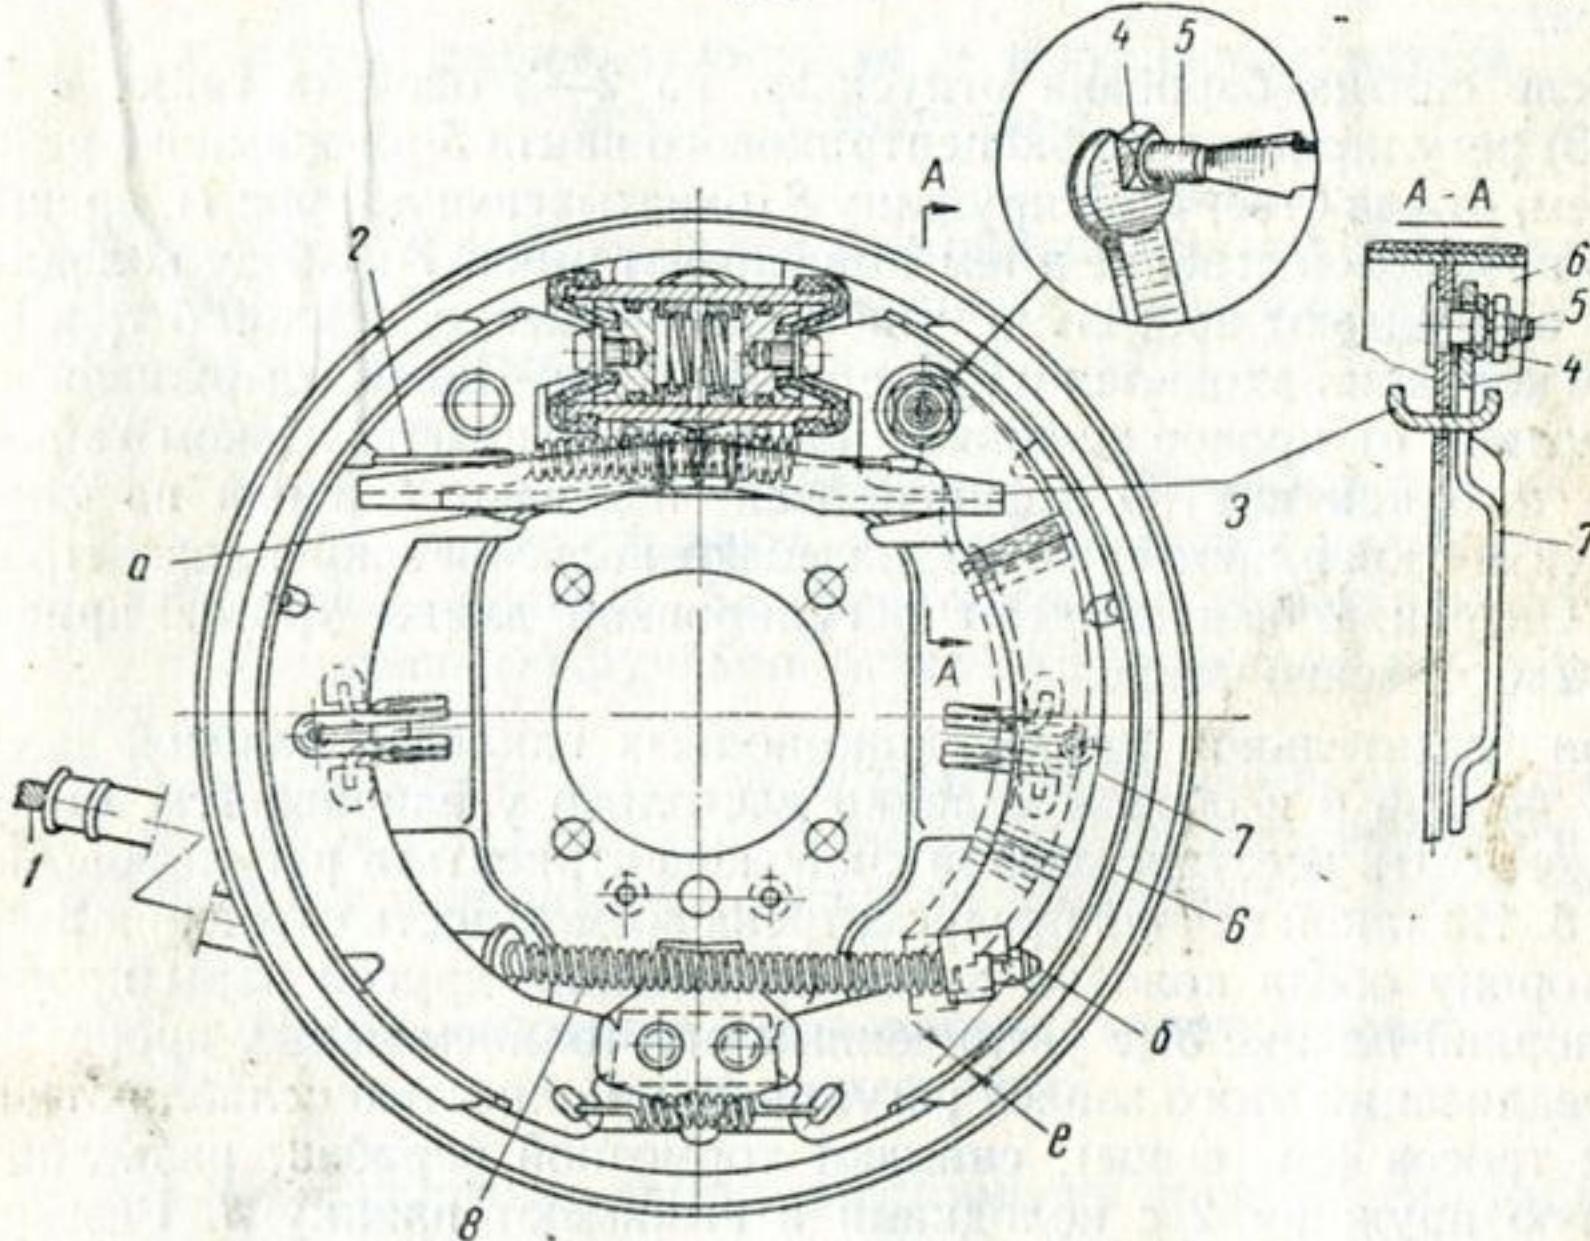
Регулировка положения разжимного рычага на задней колодке тормоза:
